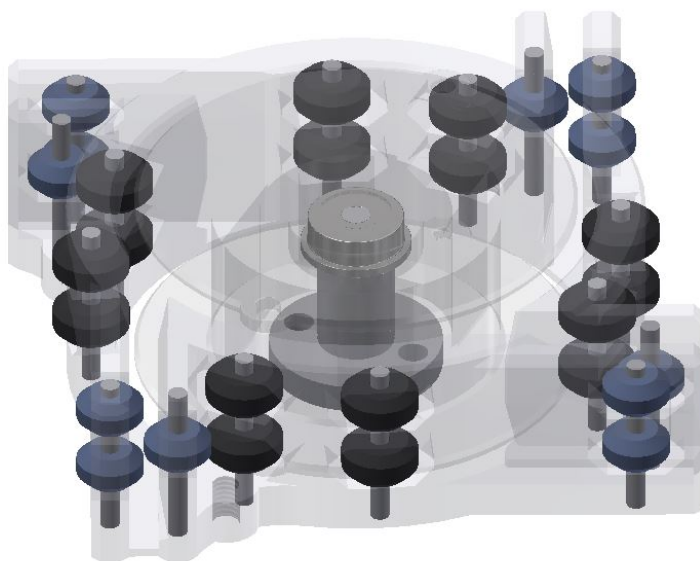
Vista de posición de rodillos, ejes y rodamiento central
